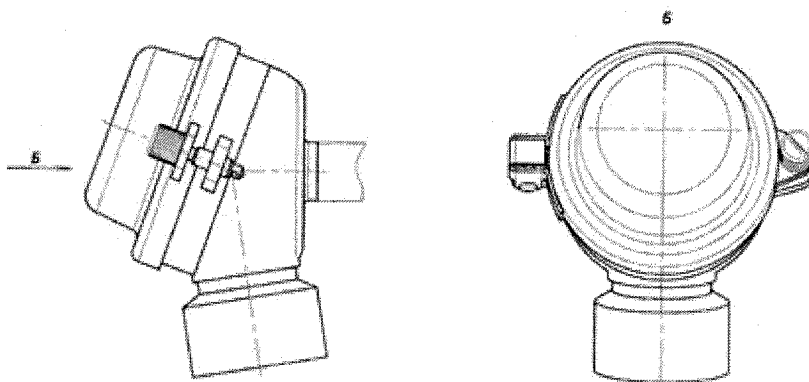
Кресленик зовнішньої частини ТХА-1690, ТХК-1690 з головкою типу БАУИ.4087234.023 СБ
